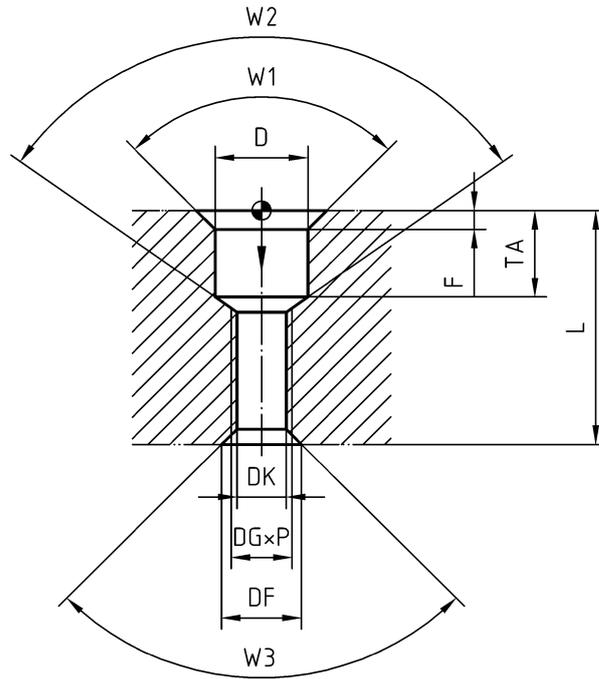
Gewindedurchgangsbohrung mit Aufbohrung
